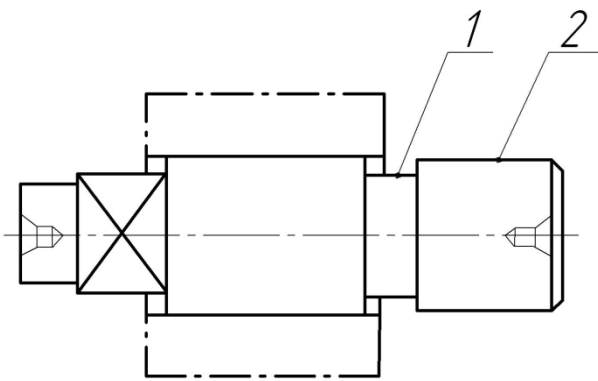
Схема цилиндрической прессовой оправки
